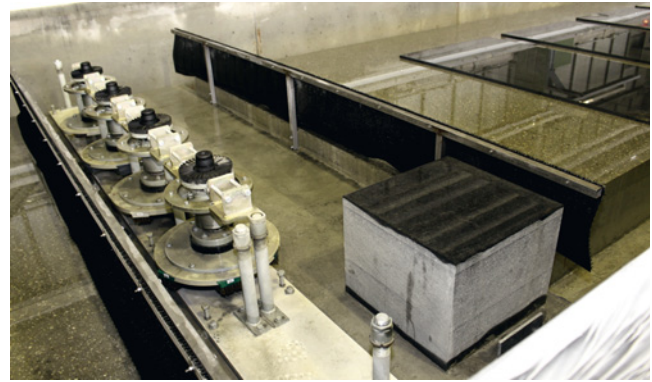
Schleifkopfmagazin mit sechs Plätzen und Auflage zur Werkzeugverschleißmessung
